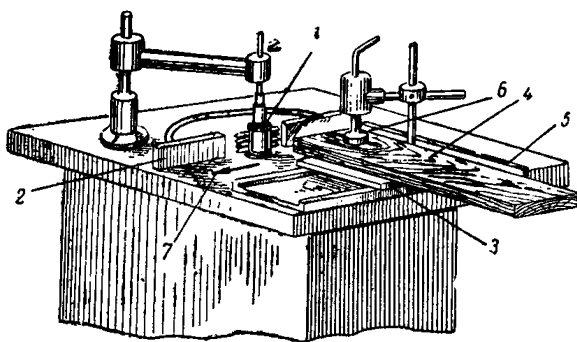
Схема нарезки зубчатых шипов на фрезерном станке
